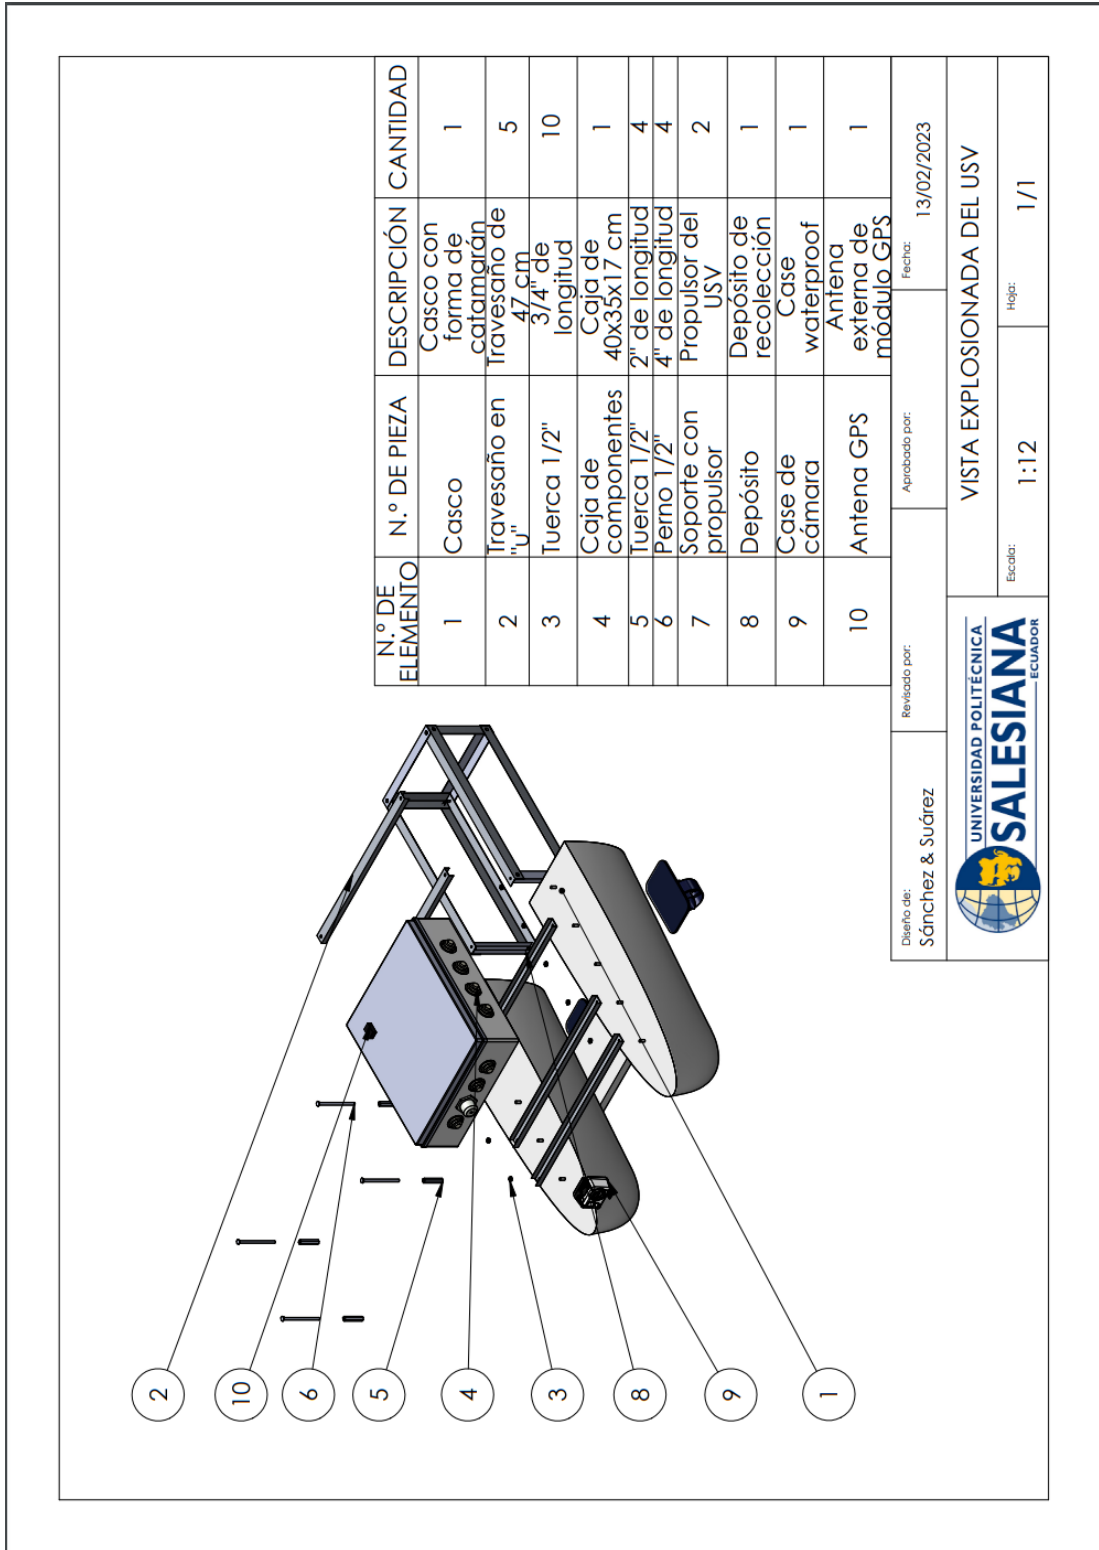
Lámina del plano explosionado del USV con su lista de macro componentes, por A. Sánchez y L. Suárez, Solidworks
